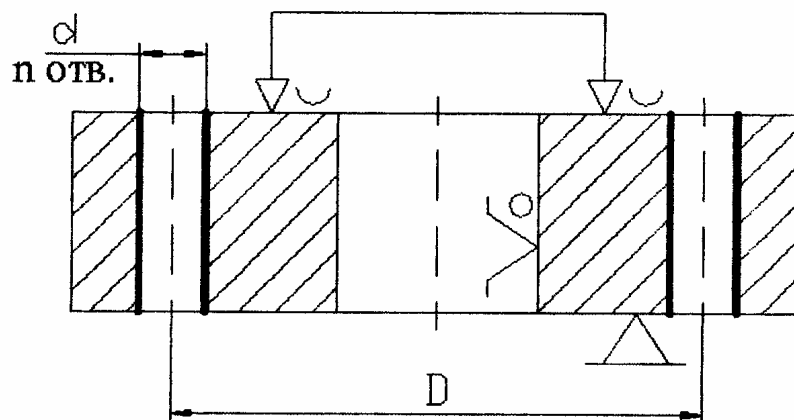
Схема установки заготовки на плоскость и цилиндрический палец
